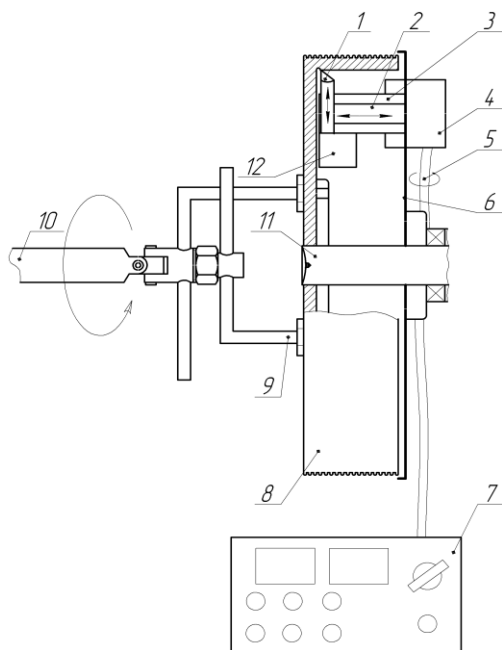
Установка для обработки рабочих поверхности тормозного барабана:
